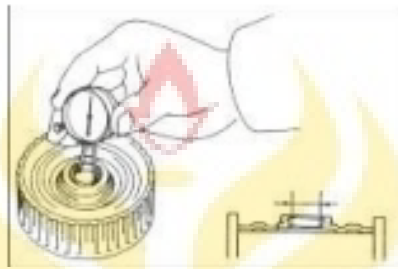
Mengukur *Planetary Pinion Gear Thrust Clearance
